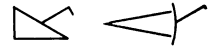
u. 65. Montageschweißzeichen.
